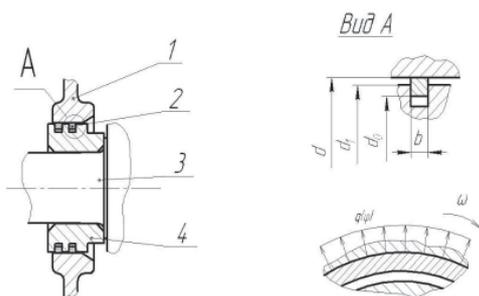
Схема узла уплотнения турбокомпрессора: 1 – корпус уплотнения; 2 – уплотнительное кольцо; 3 – вал ротора; 4 – кольцедержатель
